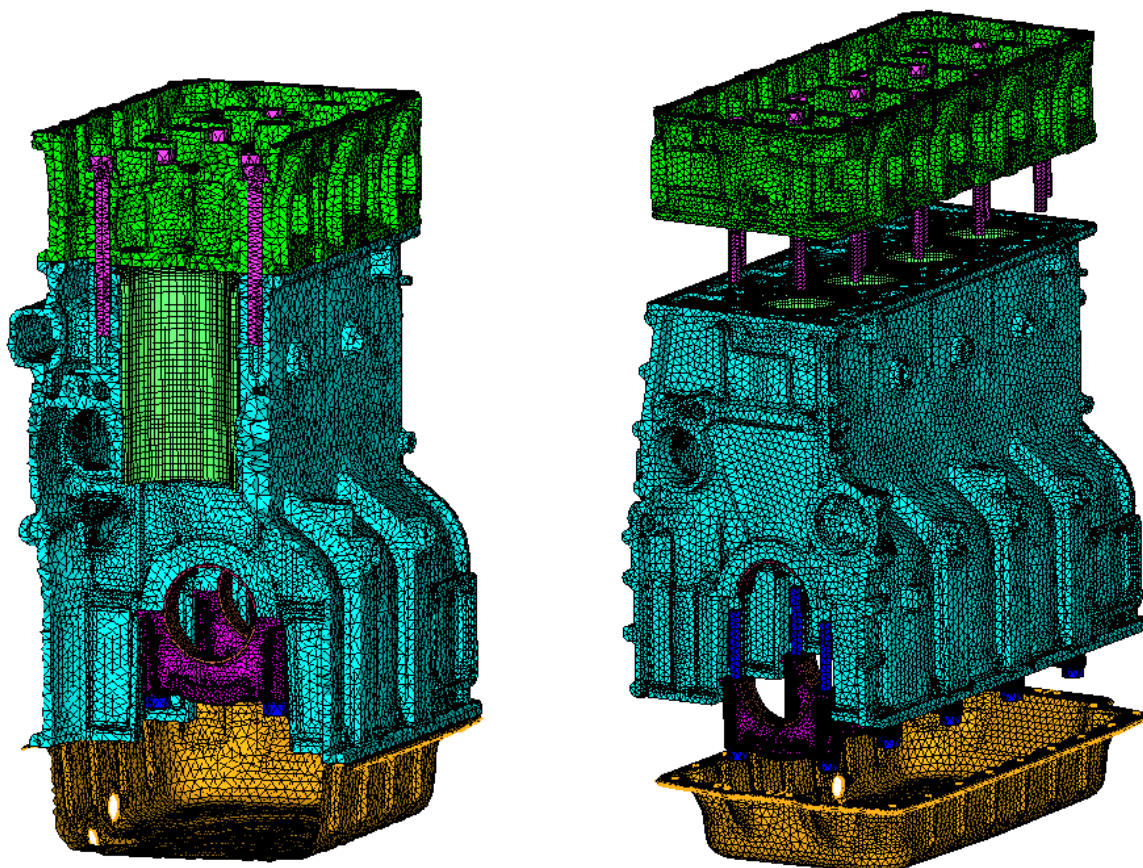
Řez konečně–prvkové sestavy motoru se spodní skříní (bedplate)
